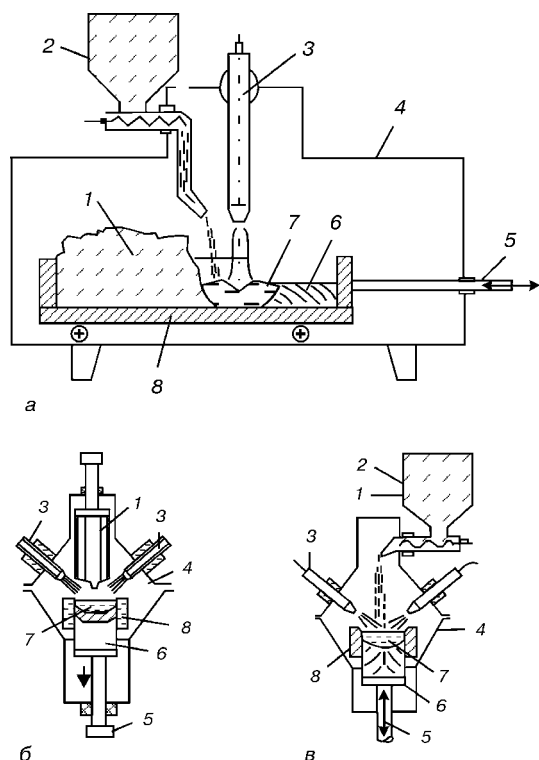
Схема плазменно-дугового компактирования дисперсных металлических материалов: *а* — на установке ОБ-1957; *б, в* — на установке УПП-3 соответственно с различными способами подачи шихты; 1 — шихта (заготовка); 2 — бункер шнекового питателя; 3 — плазмотрон; 4 — плавильная камера; 5 — шток привода перемещения; 6 — литок; 7 — металлическая ванна; 8 — кристаллизатор
